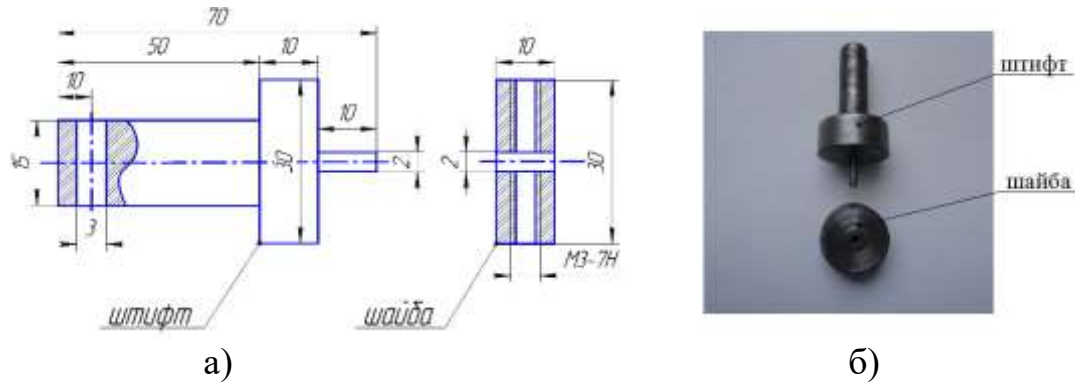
Образец для исследования адгезионной прочности ЭМ-покрытий: а) схема; б) общий вид.
